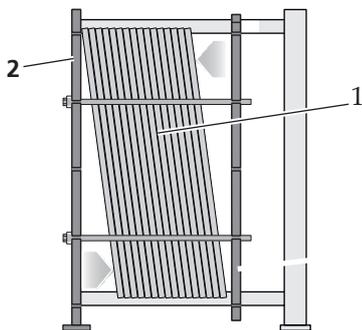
c – Positionnement incliné des plaques EC reposant sur le haut de la plaque fixe
